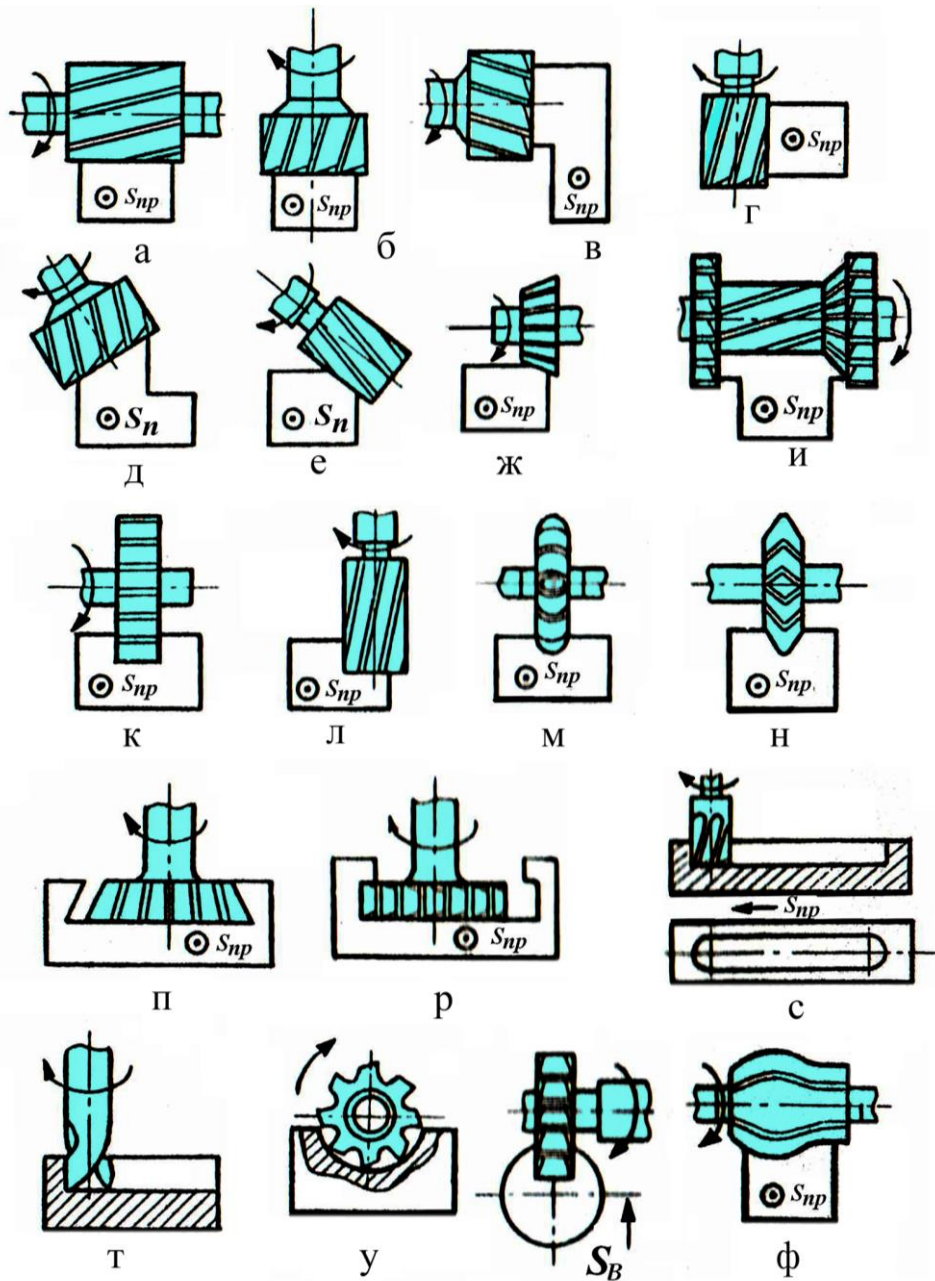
Схеми обробки поверхонь заготовок на горизонтально- та вертикально-фрезерних верстатах
